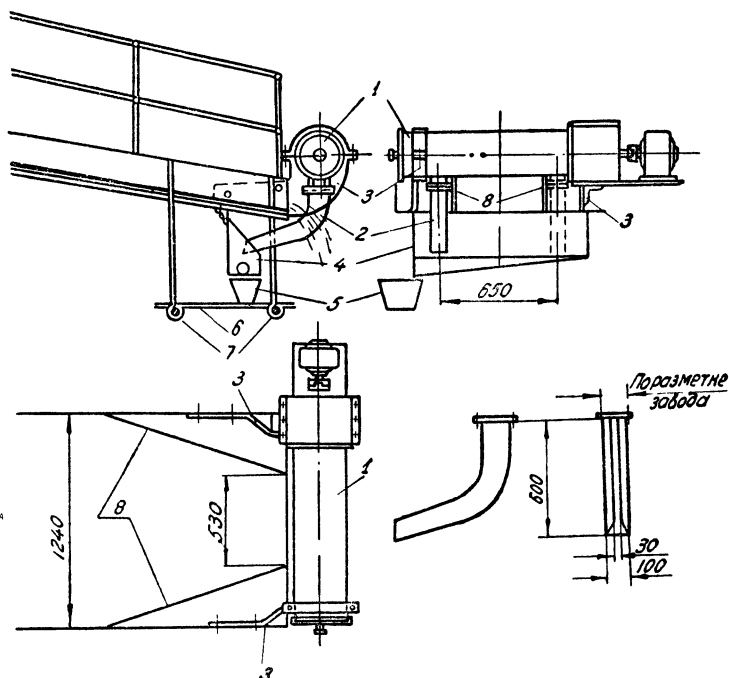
Схема установки автоматических пробоотборников на шлюзах:
